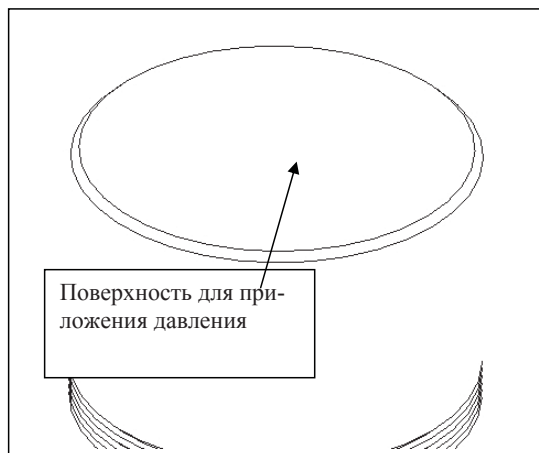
Общий вид модели, поверхность для приложения давления
